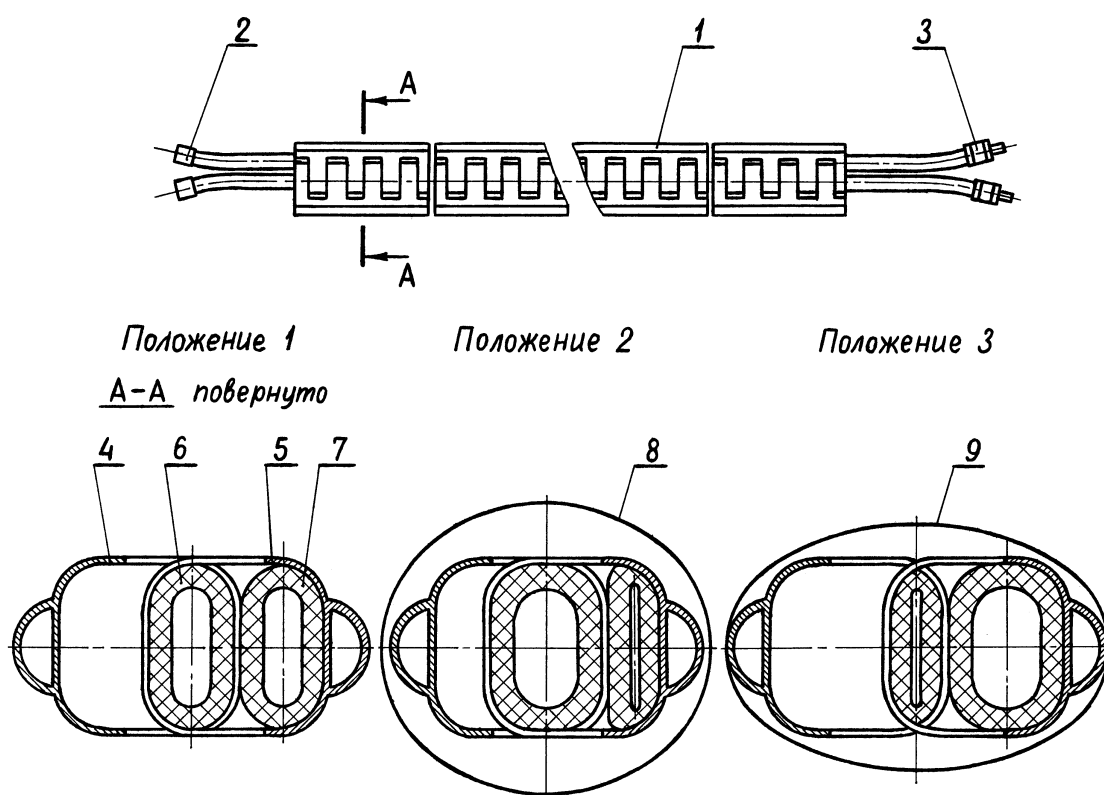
Приспособление для осадки камер дипольных магнитов: 1 — приспособление в сборе; 2 — наконечник с заглушкой; 3 — гидроразъем; 4 — полукассета левая; 5 — полукассета правая; 6 — рукав дюритовый левый; 7 — рукав дюритовый правый; 8 — камера типа МА до осадки; 9 — камера МА, осажённая для установки в магнит.
